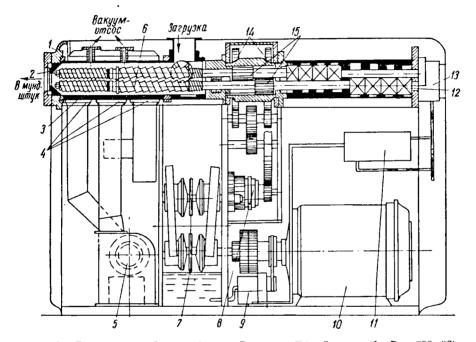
Двухчервячный пресс фирмы Вернер и Пфлейдерер (L:D=700:83): I—головка; 2, 3—корпус; 4—нагревательные элементы корпуса; 5—вентилятор для охлаждения корпуса, 6—загрузочный червяк; 7—варнатор; 8—редуктор; 9—насос для циркуляционной смазки; 10—электродвигатель мощностью 28 квт; 11—раднатор водяного охлаждения маслосистемы, 12—упорный узел; 13—охлаждающие устройства червков (барботеры); 14—сдвоенная щестерня с наружным и внутренним сцеплениями; 15— шестерни с наружным сцеплением.
